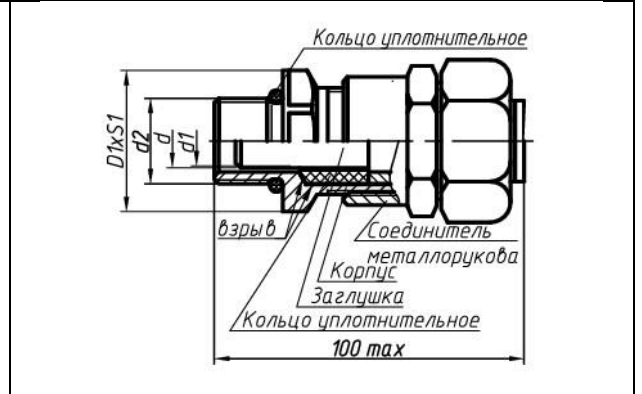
ExdKBV-M с соединителем металлорукава — Герда-СГ с внутренней резьбой. Размеры см в таблице 8
